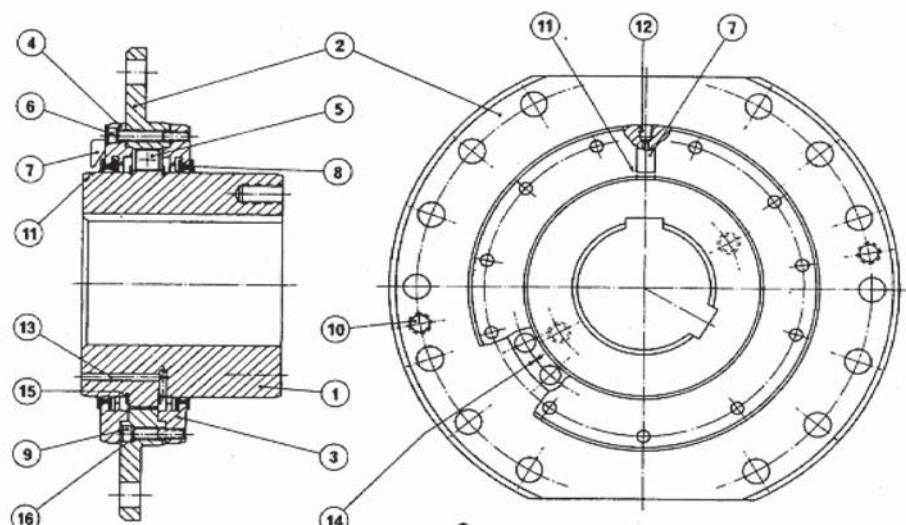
Конструкция стандартной цилиндрической муфты типа TCB фирмы "JAURE".
